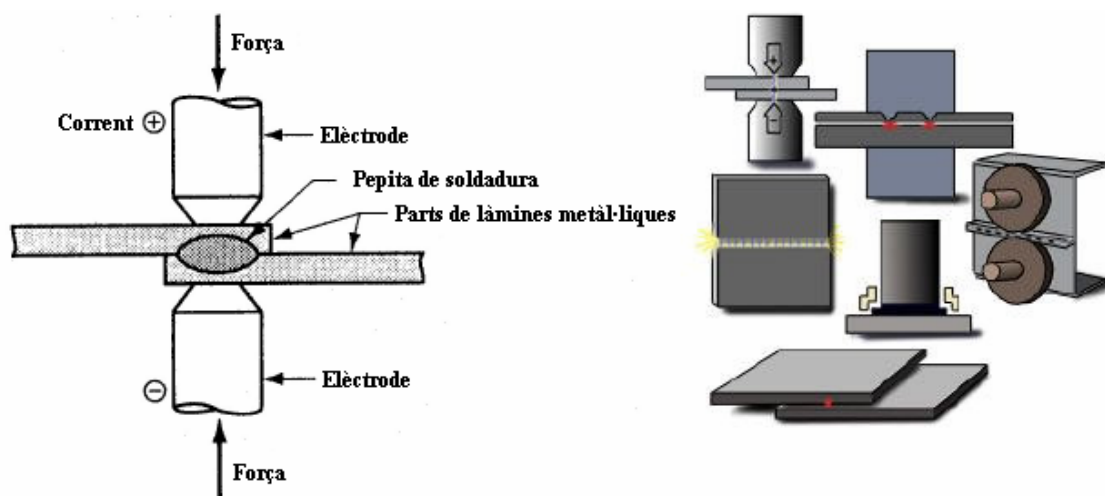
Soldadura per resistència mostrant els components en la soldadura de punts.
